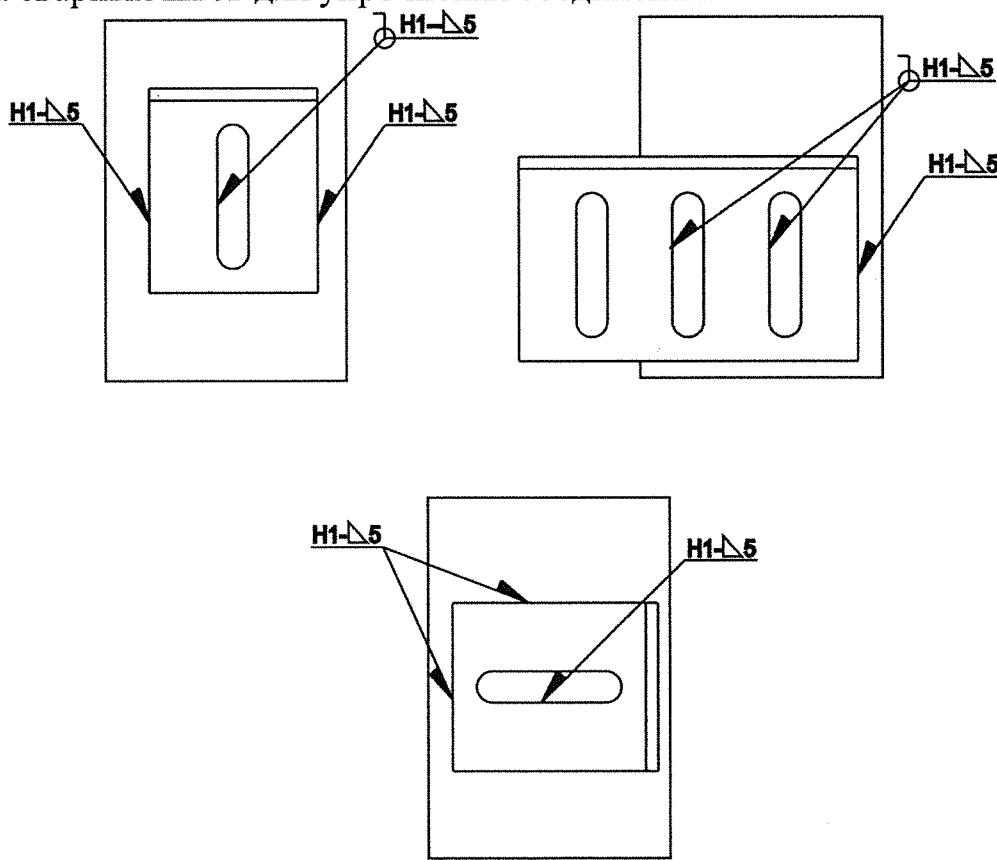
Расположение сварных швов на уголках.
